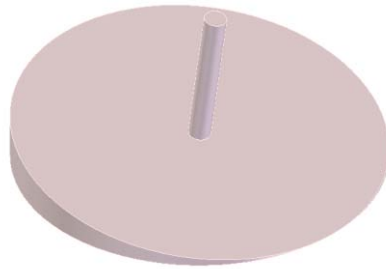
Base circular asimétrica para el carrete rebobinador.
